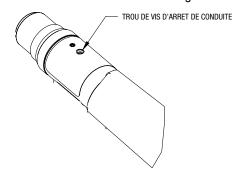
Trou D'acces a la Vis D'arret de Conduite
